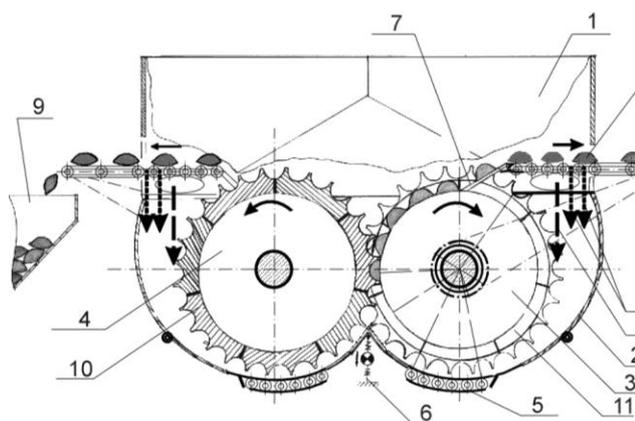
Конструкция вальцевого пресса с протяженной зоной предварительного уплотнения шихты:
